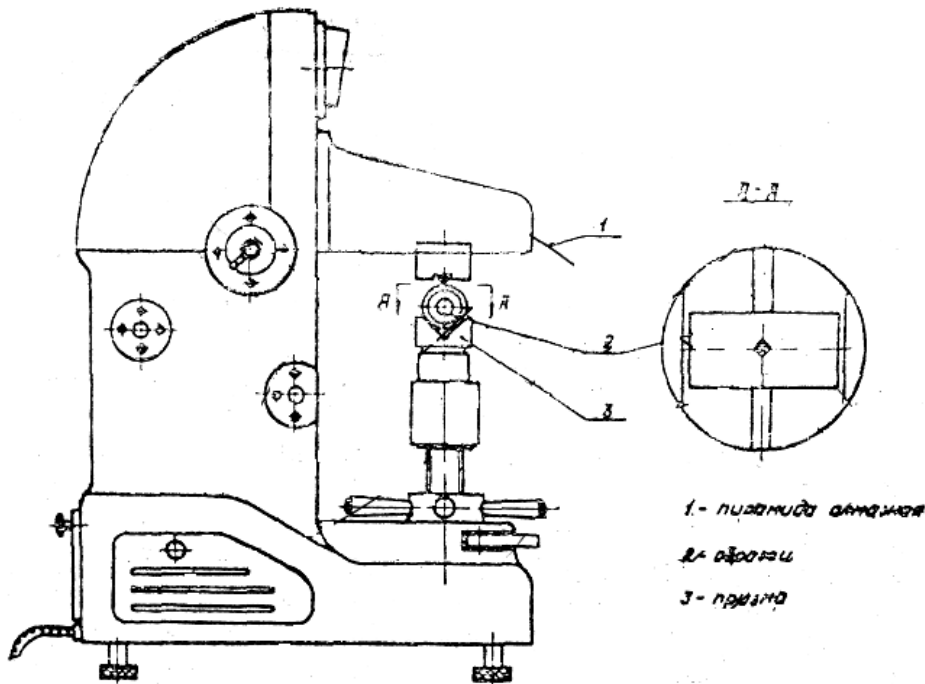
Установка образца для нанесения отпечатка на ТП-2.
